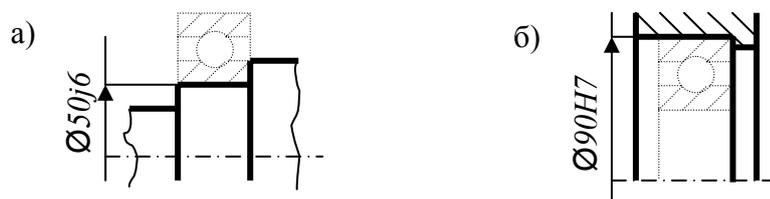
Обозначение посадок мест под подшипники а – на валу; б – в отверстии корпуса
